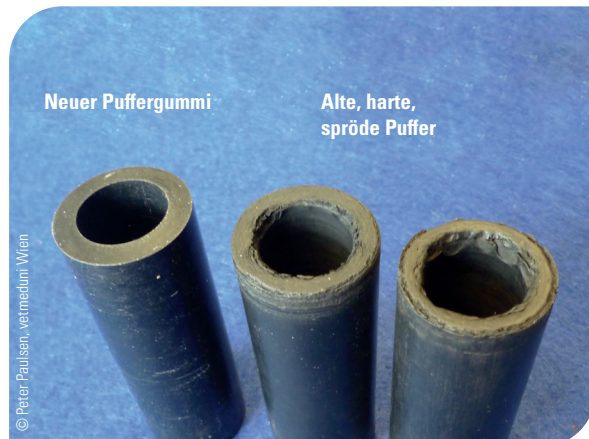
Alte Gummipuffer müssen ausgetauscht werden
